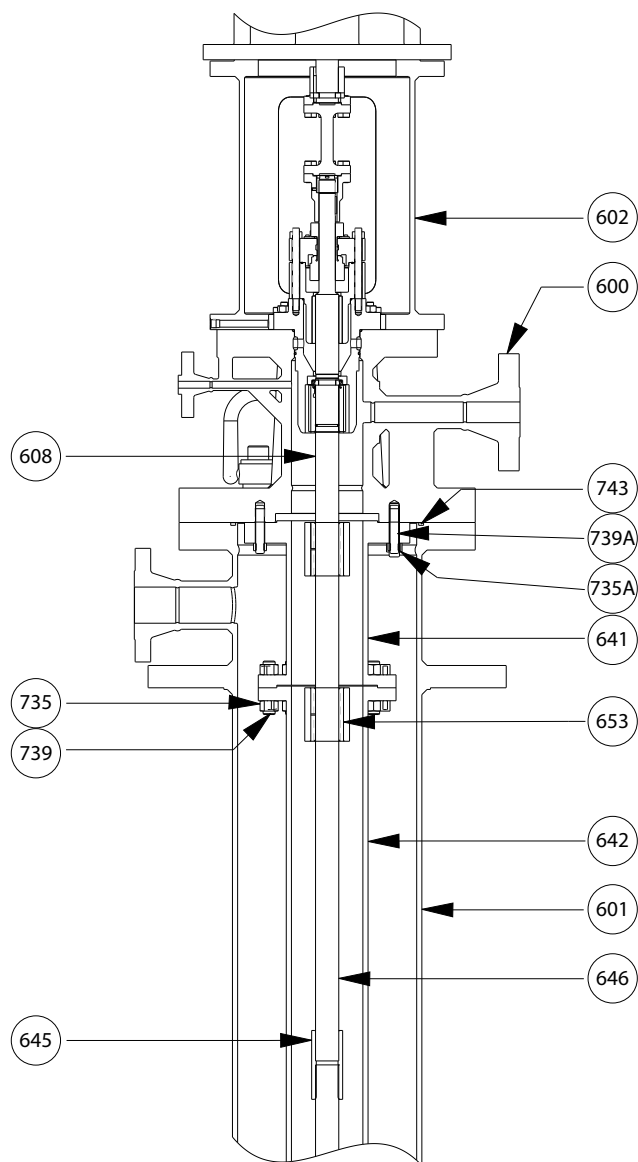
Узел камеры рабочего колеса, деталь А — вариант 1
